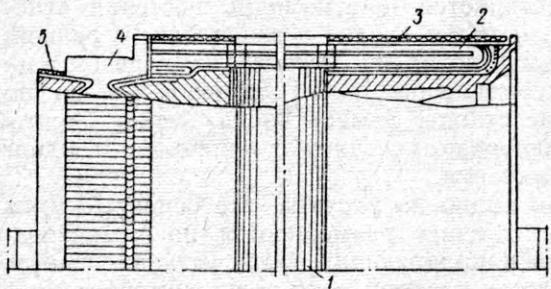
Общий вид приспособления для намотки бандажей из стеклоленты:
